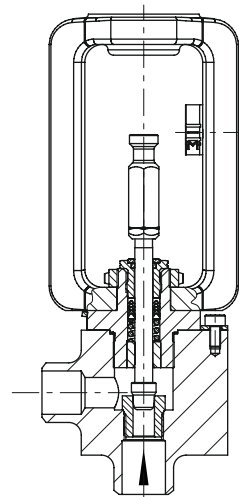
Hochdruckventil Typ 3252 als Eckventil mit Anschweißenden
